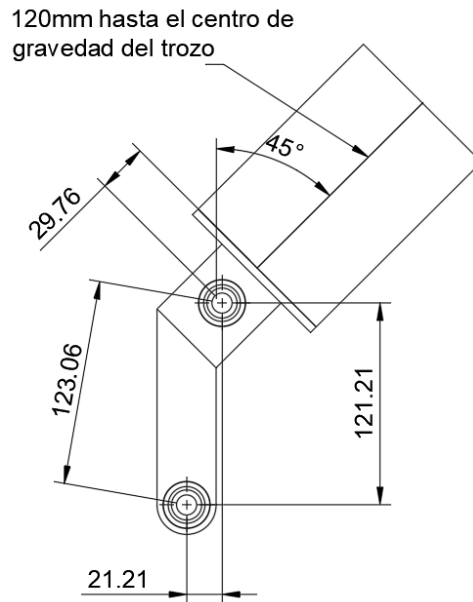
Boceto de la base basculante del posicionador de trozos.
